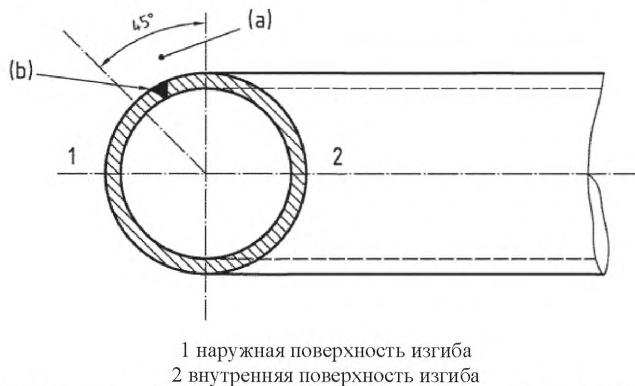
Оптимальный диапазон для продольного сварного шва при изгибе
